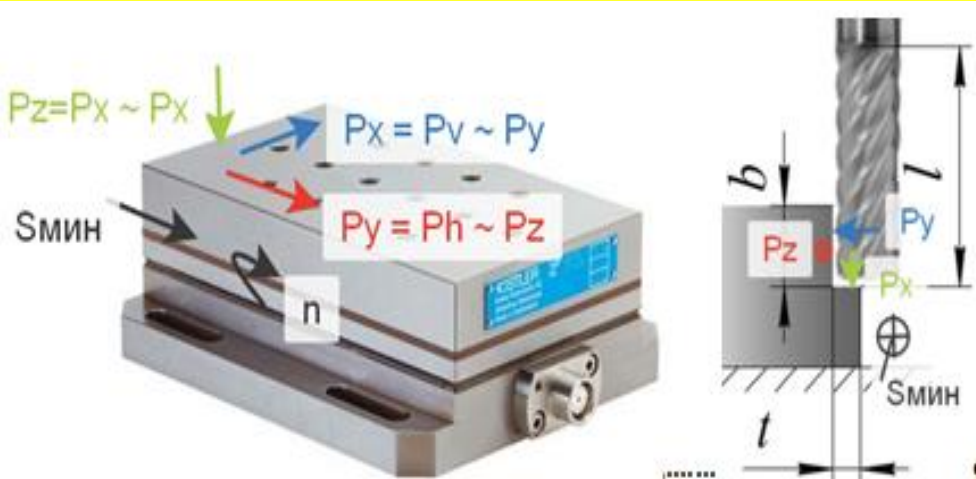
Составляющие силы резания при фрезеровании концевой фрезой с использованием токарного динамометра Kistler.
